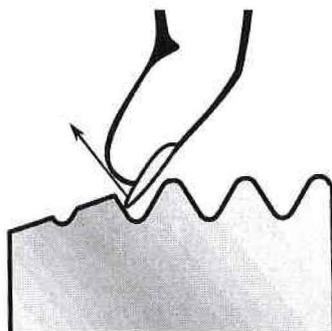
Проверка валика металла на фаске ниппеля или муфты
